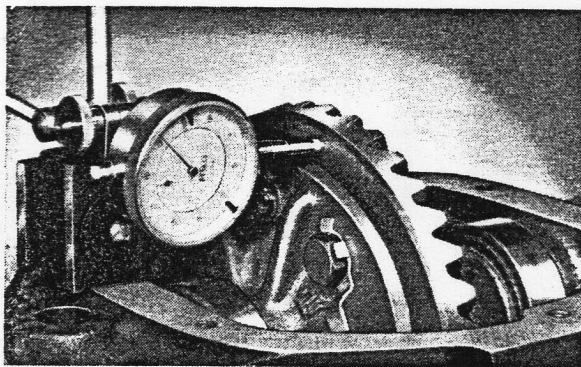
Ausmessen des Axialspiels des Ausgleichgetriebes
